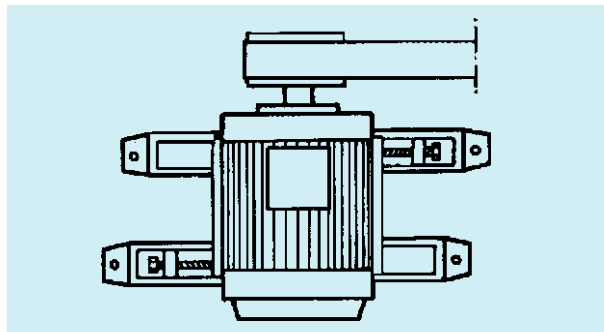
Lage der Gleitschienen zum Ausrichten des Motors
